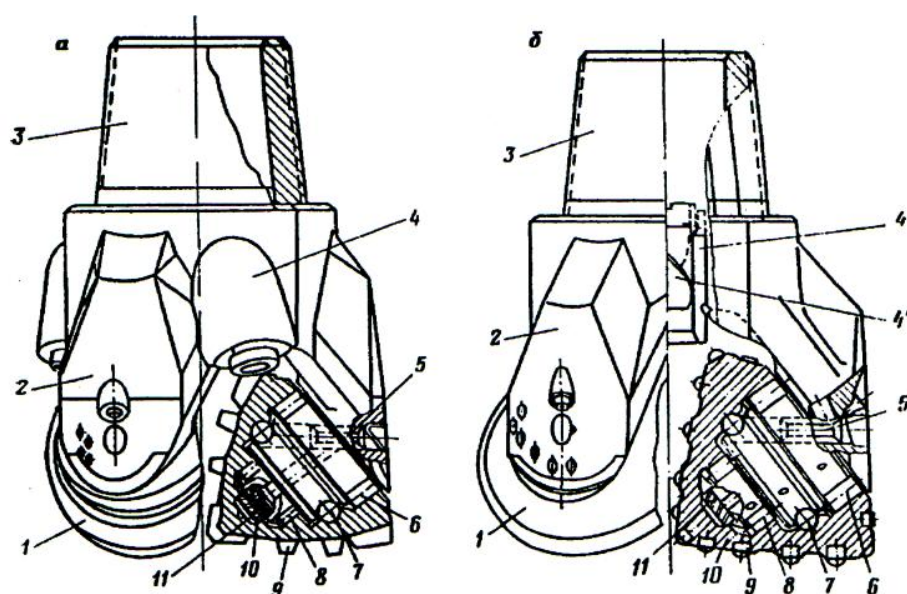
Конструктивные схемы трехшарошечных долот: а – зубчатого с фрезерованным вооружением шарошек и периферийной продувкой; б – штыревого (твердосплавные вставки) и центральной продувкой: 1 – шарошка; 2 – лапа долота; 3 – ниппель с резьбой; 4 – периферийный (а) и центральный (б) продувочные каналы; 5 – канал для подачи шариков замка; 6 – роликовый подшипник опоры; 7 – замковый шариковый подшипник; 8 – роликовый подшипник опоры; 9 – фрезерованные зубья шарошки (а) и твердосплавные штыри (б); 10 – корпус шарошки; 11 – опорная пятка опоры шарошки
